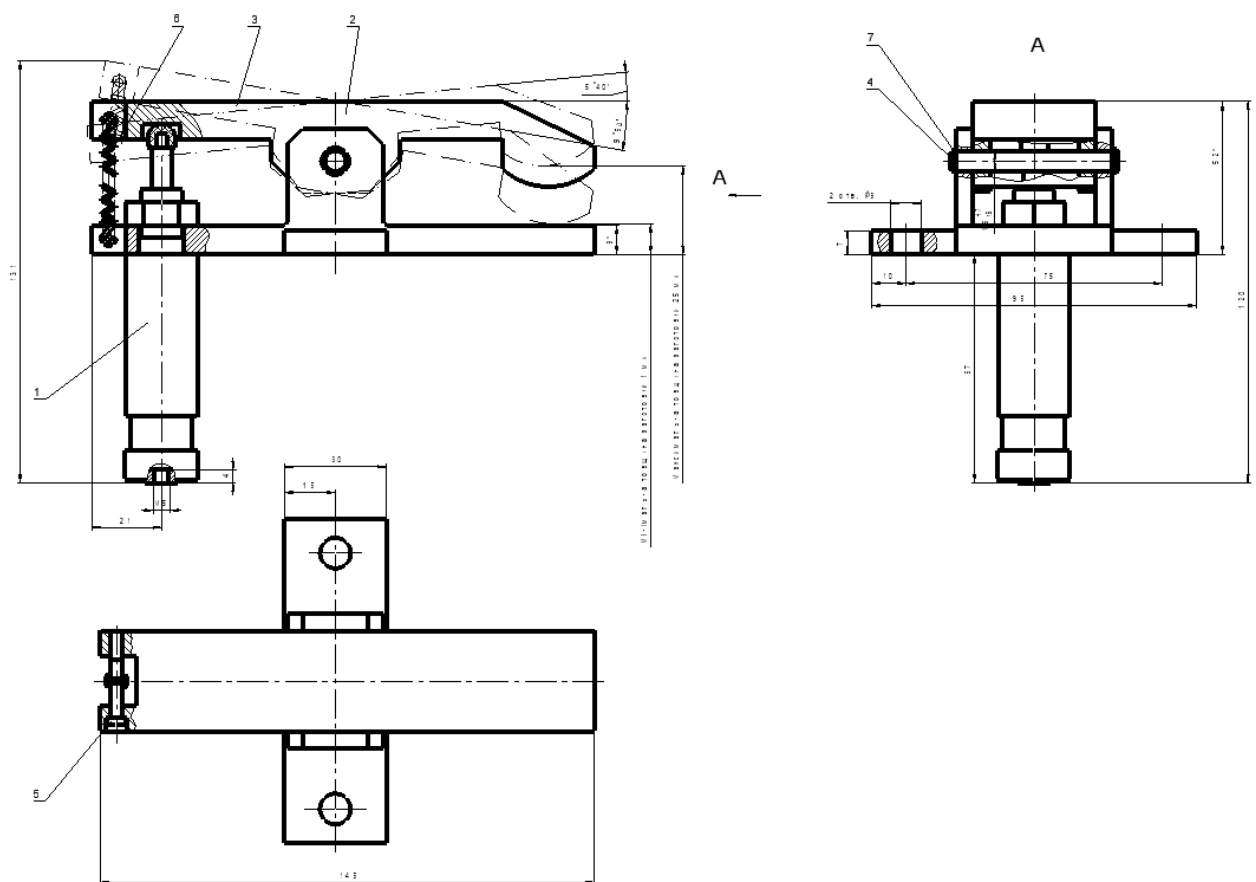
Затискач: 1 – зворотна пружина; 2 – шток пневмоциліндру; 3 – важіль;
